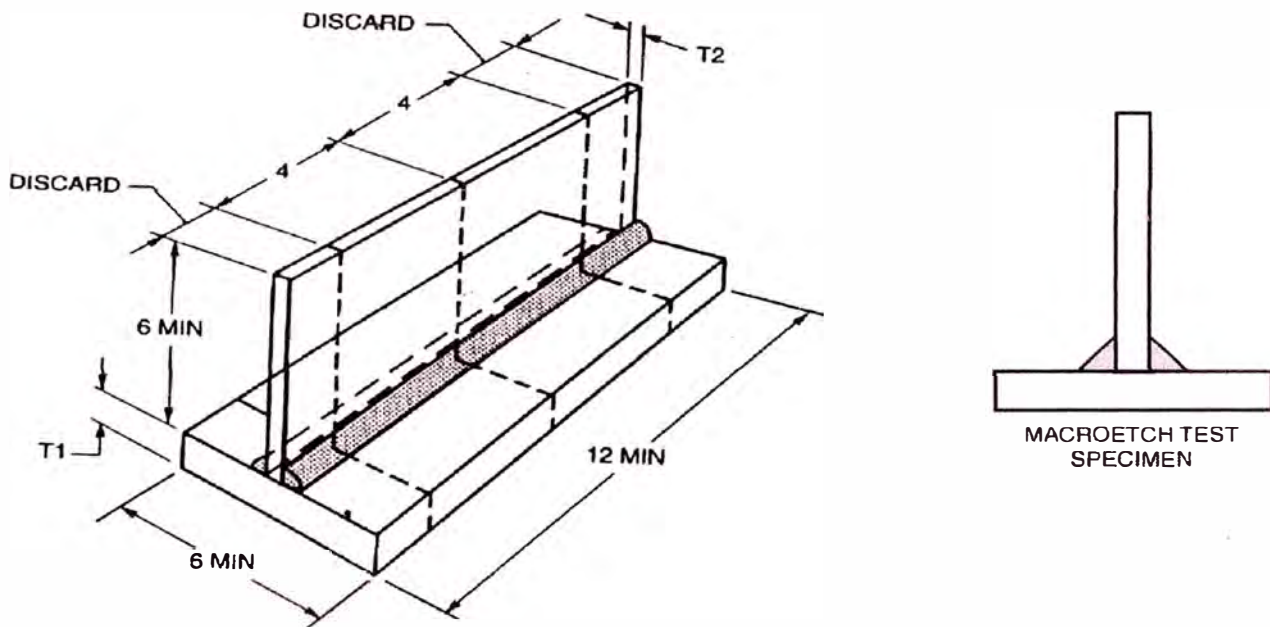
Probeta Para Calificación De Procedimiento De Soldadura En Filete.
